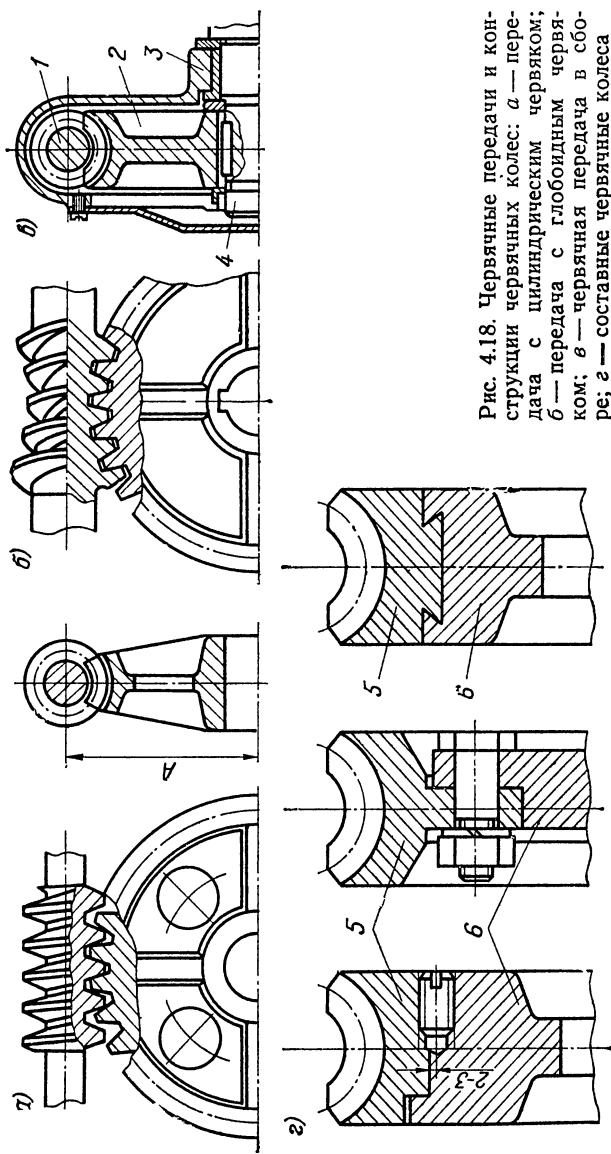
Червячные передачи и конструкции червячных колес: а — передача с цилиндрическим червяком; б — передача с глобоидным червяком; в — червячная передача в сборе; г — составные червячные колеса
